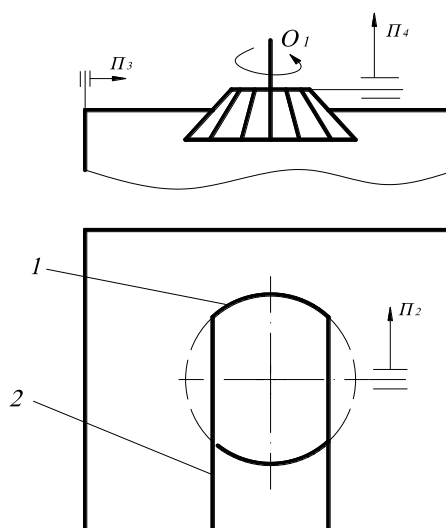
Схема фрезерування «ластівкового хвоста» фасонною фрезою
